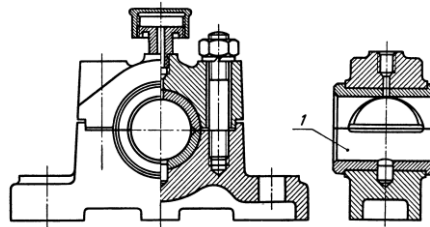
Подшипник с разъемным корпусом и вкладышем
